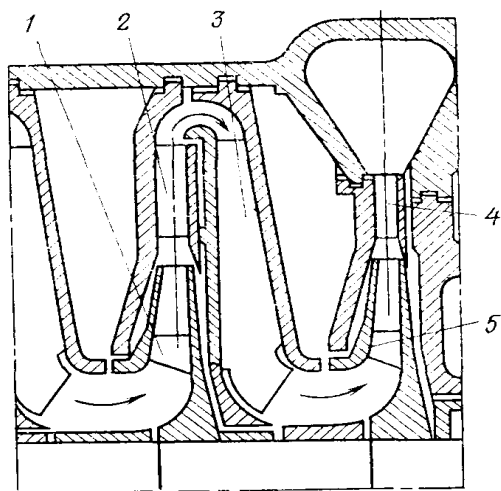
Схема промежуточной и концевой ступеней центробежного компрессора
